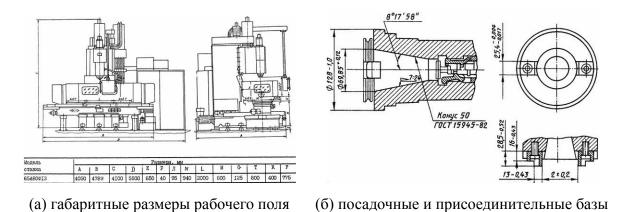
Посадочные и присоединительные размеры станка 65А80
